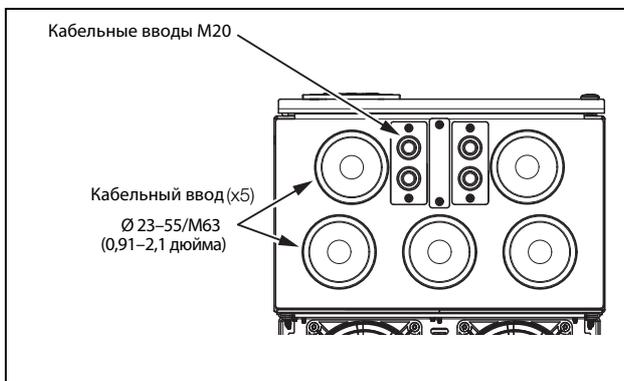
Кабельный интерфейс для подключения электрической сети, электродвигателя, DC+/DC-, тормозного резистора и связи, устройство Emotron FDU модели 48-365-54 (размер корпуса FA).
